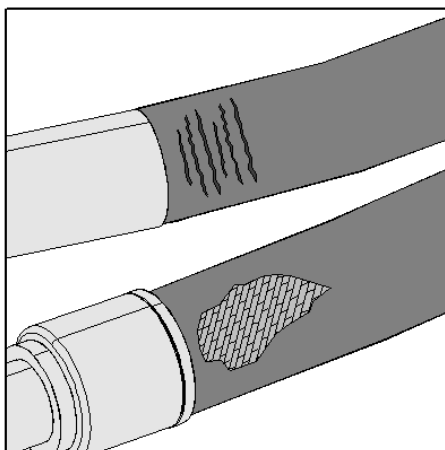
Трещины и разрезы вплоть до армирующей оплетки или видна армирующая оплетка вследствие повреждения защитной оболочки
